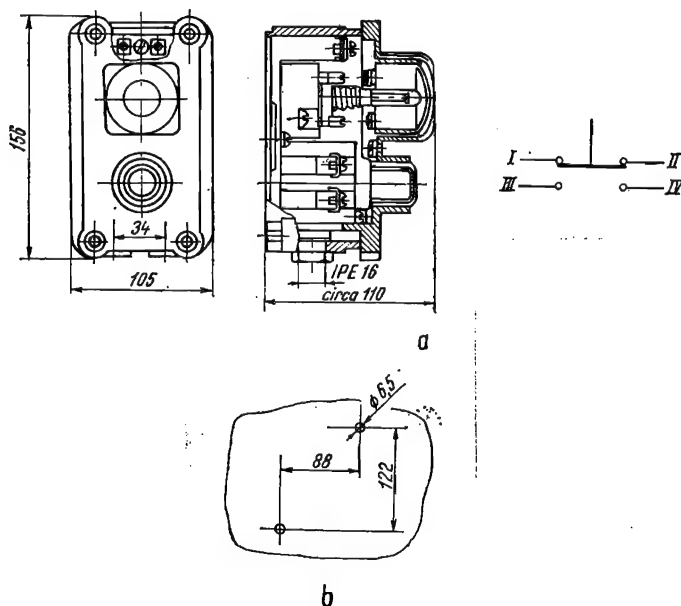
Buton cu lampă inclusă în execuție antiexplozivă cod 3751:
